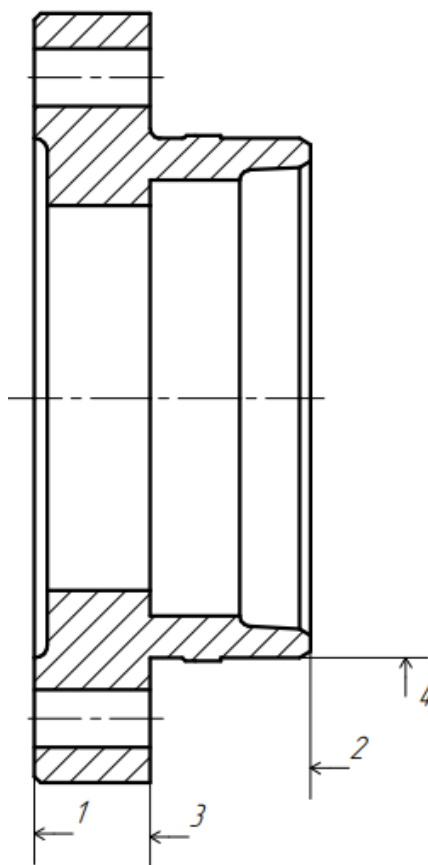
Ескіз деталі «Кришка підшипника»
